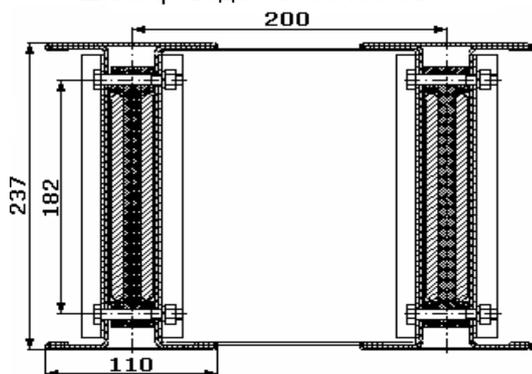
Поперечное сечение шинопровода на ток 3200А.
